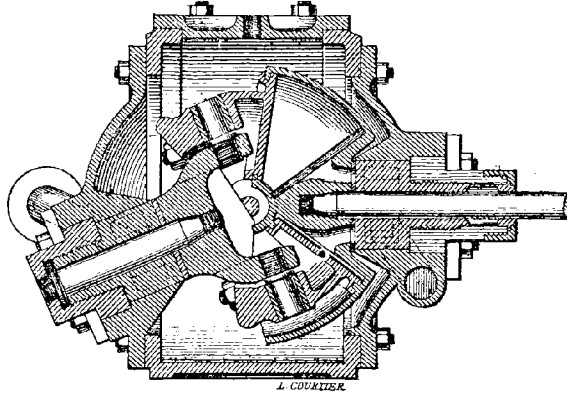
Machine rotative Fielding et Platt (coupe).
